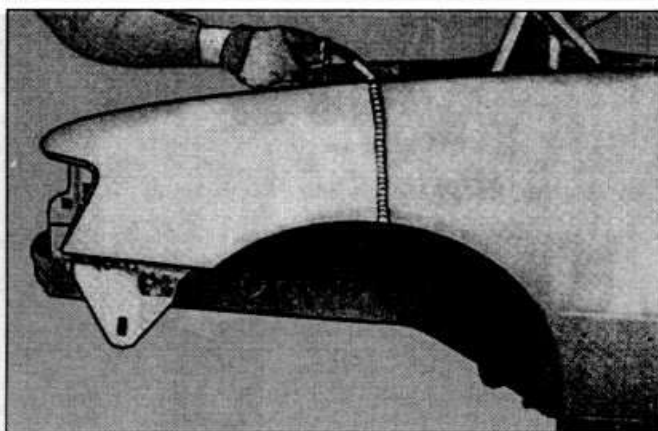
Вид восстановленной части переднего крыла и сварного шва
